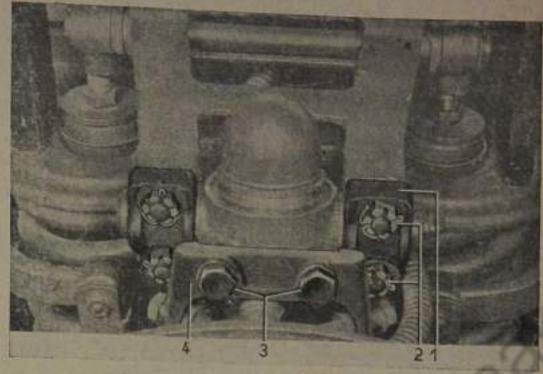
Lagerung für oberen Lagerzapfen abschrauben
